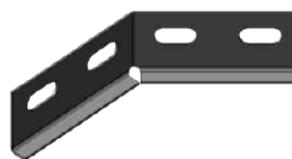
Соединитель регулируемый для лестничного лотка (1,2) ПжТехКабель
